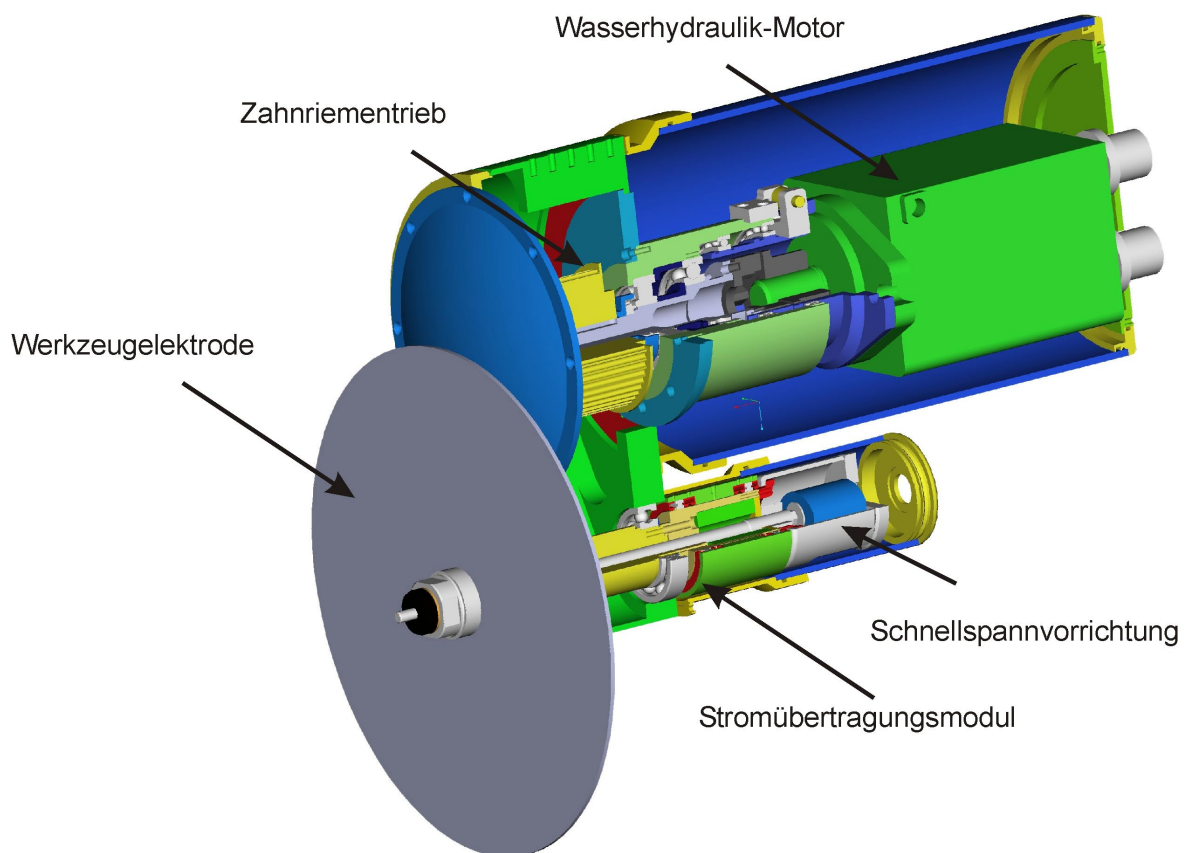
3-D CAD-Model des entwickelten CAMG-Werkzeug
